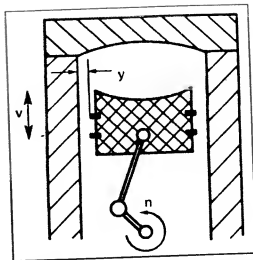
Поперечное сечение цилиндра двигателя и поршня для оценки параметров течения смазочного масла
